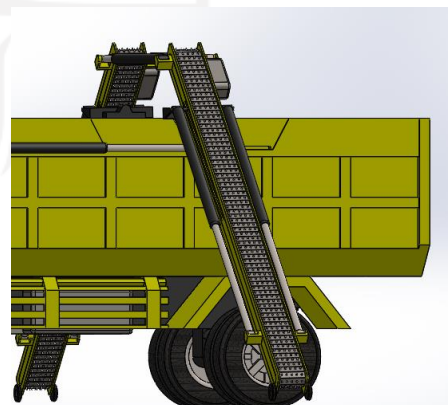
6 Tampak Samping (Komponen *Slat Conveyor* Pada Alat)
